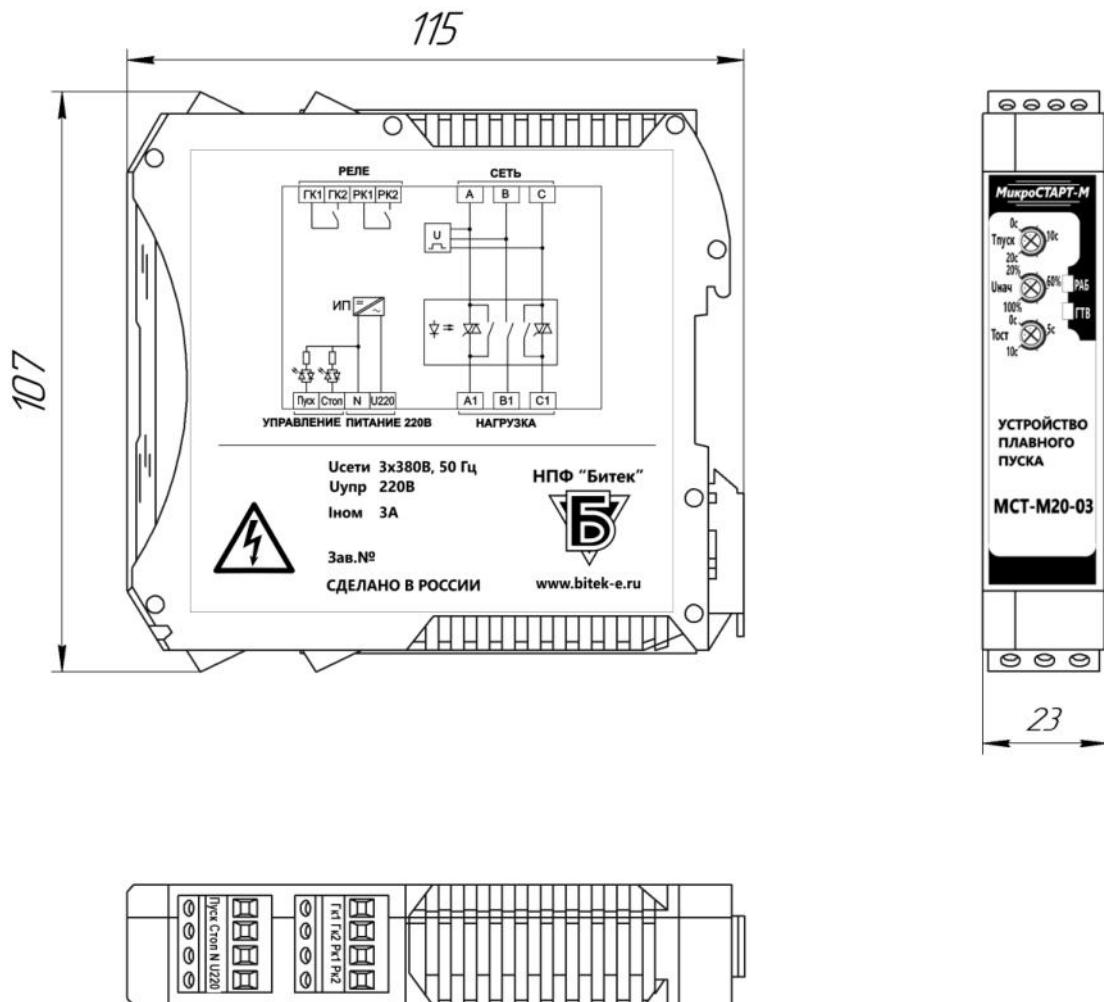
Габаритно-установочные размеры МСТ-М2х-03
